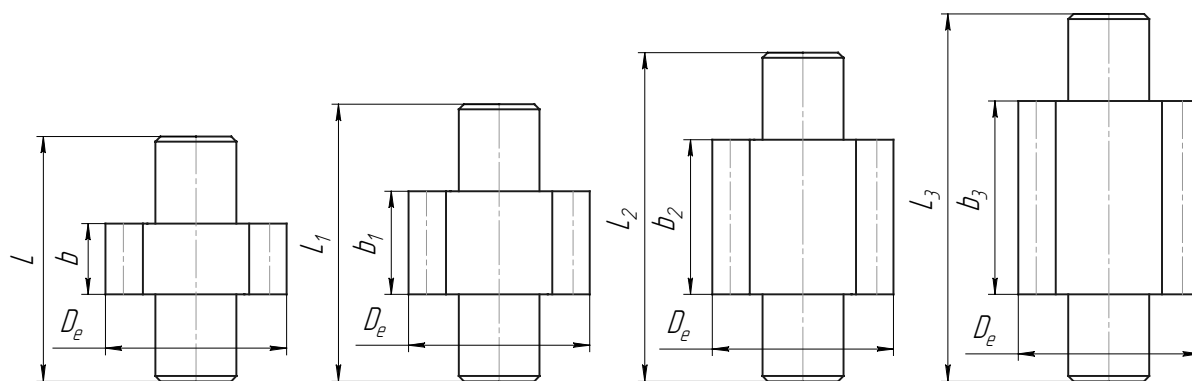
Эскизы шестерен одного типоразмерного ряда, отличающихся шириной венцов
